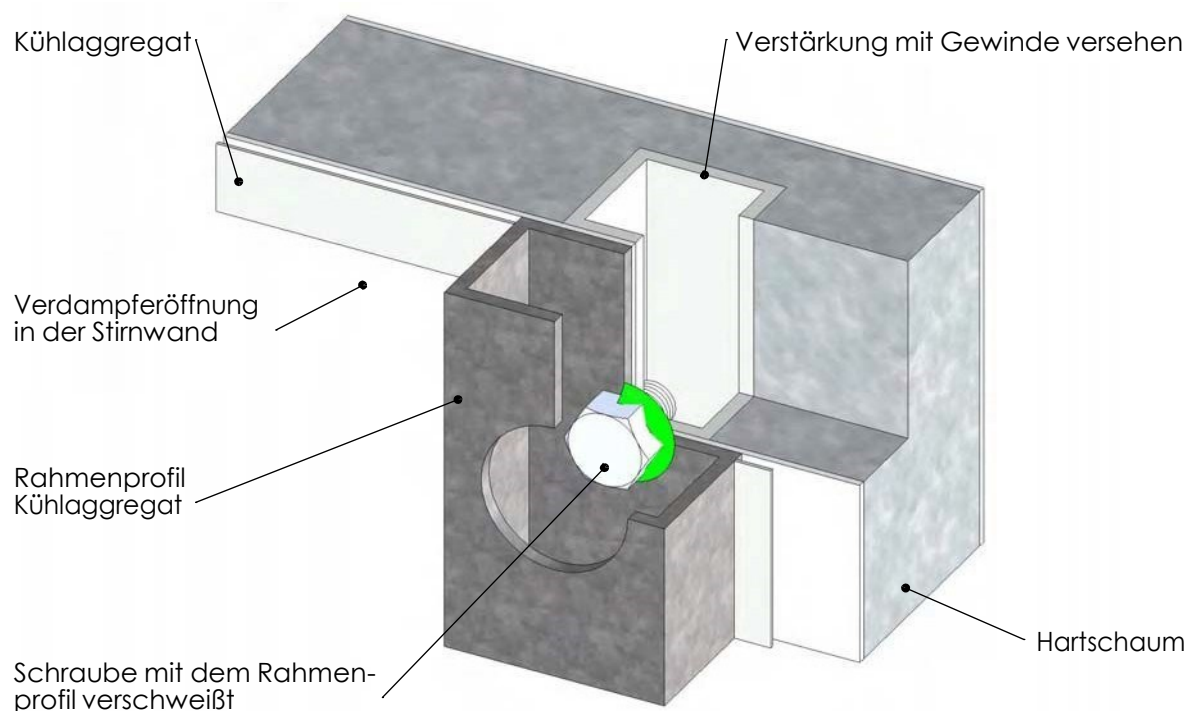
Sicherung mit von außen verschweißten Schrauben
